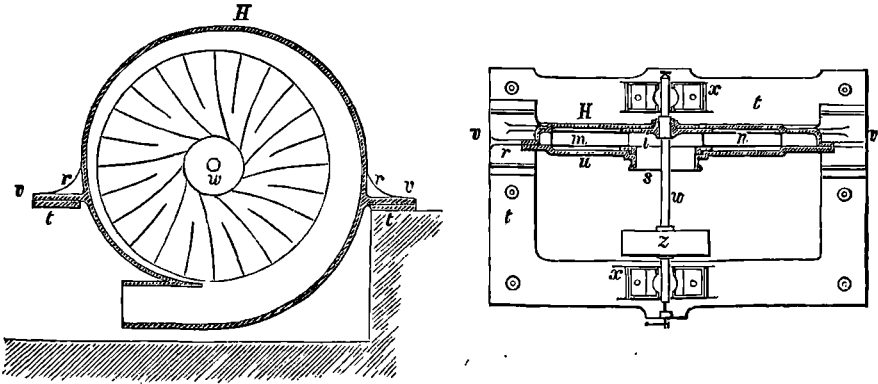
et 628. — Ventilateur centrifuge de Rittinger.
